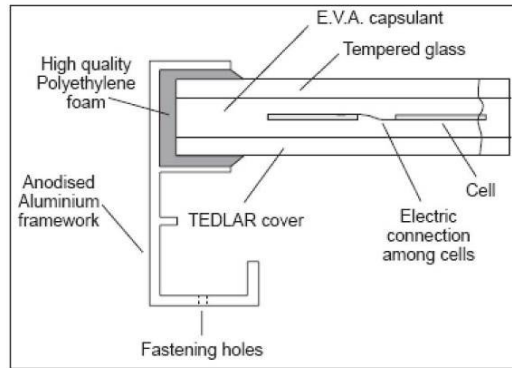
Sezione del modulo fotovoltaico tipo.
